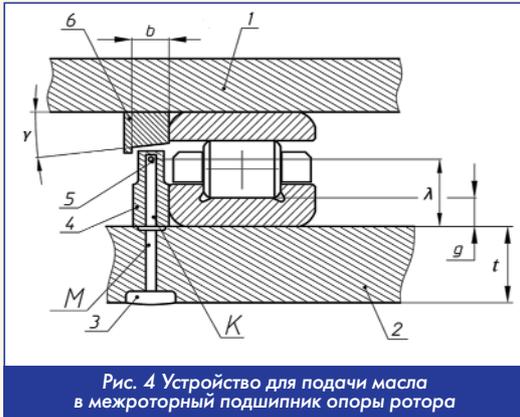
Устройство для подачи масла в межроторный подшипник опоры ротора
